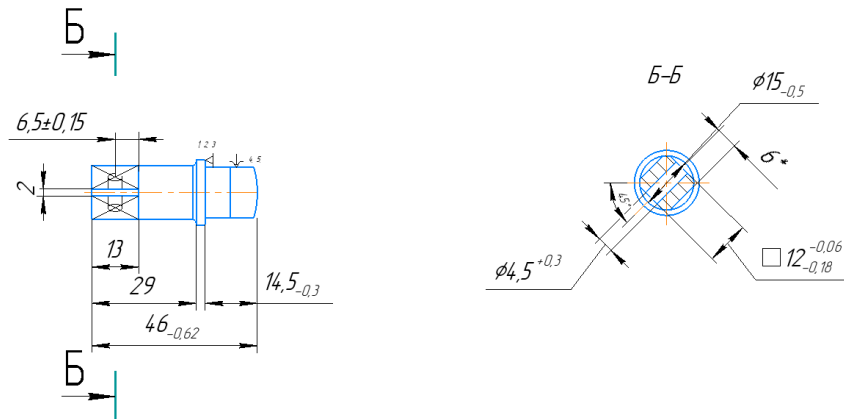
Схема базування заготовки в трикулачковому патроні
